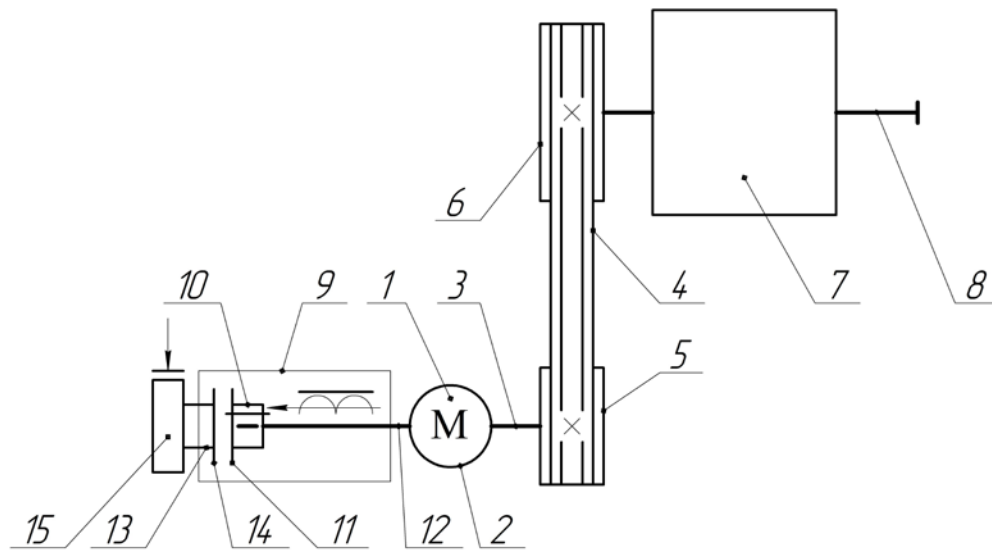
Кінематична схема привода в'язальної машини: 1 – електродвигун; 2 – корпус; 3 – вал; 4 – пасова передача; 5 – ведучий шків; 6 – ведений шків; 7 – блок механічних передач; 8 – приводний вал; 9 – електромагнітна фрикційна муфта; 10 – ведуча півмуфта; 11 – диски ведучої півмуфти; 12 – вал; 13 – ведена півмуфта; 14 – диски веденої пів муфти; 15 – гальмо
